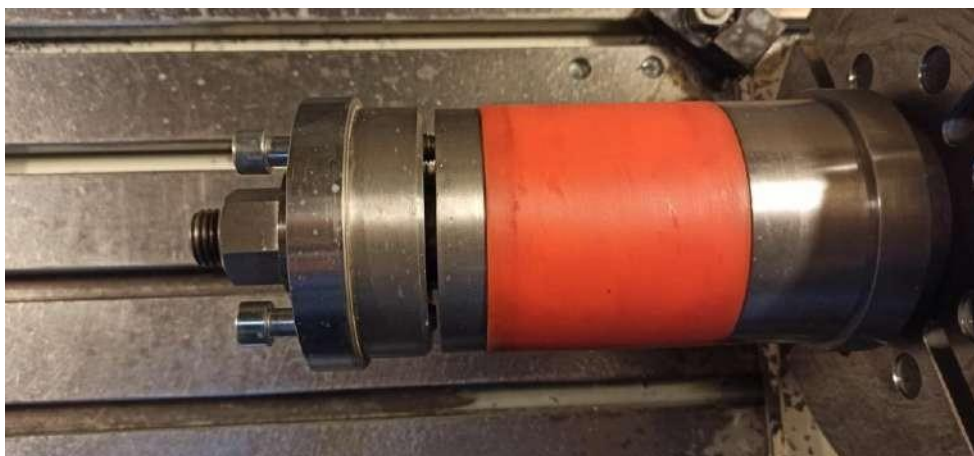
Фото оправки по патенту [9], установленной в поворотной оси фрезерного станка
